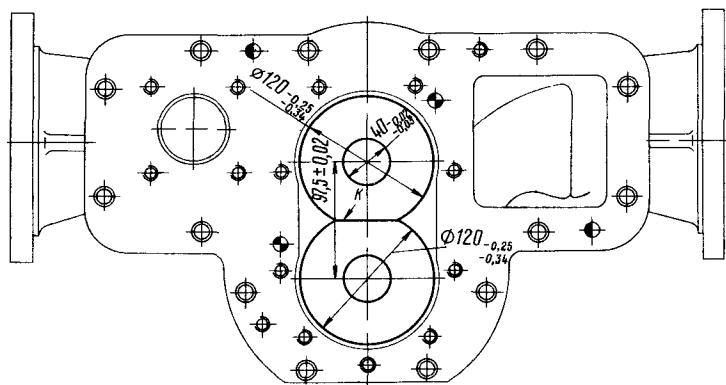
Технологические зубчатые колеса для центровки подшипниковых планок масляного насоса дизеля типа Д100
